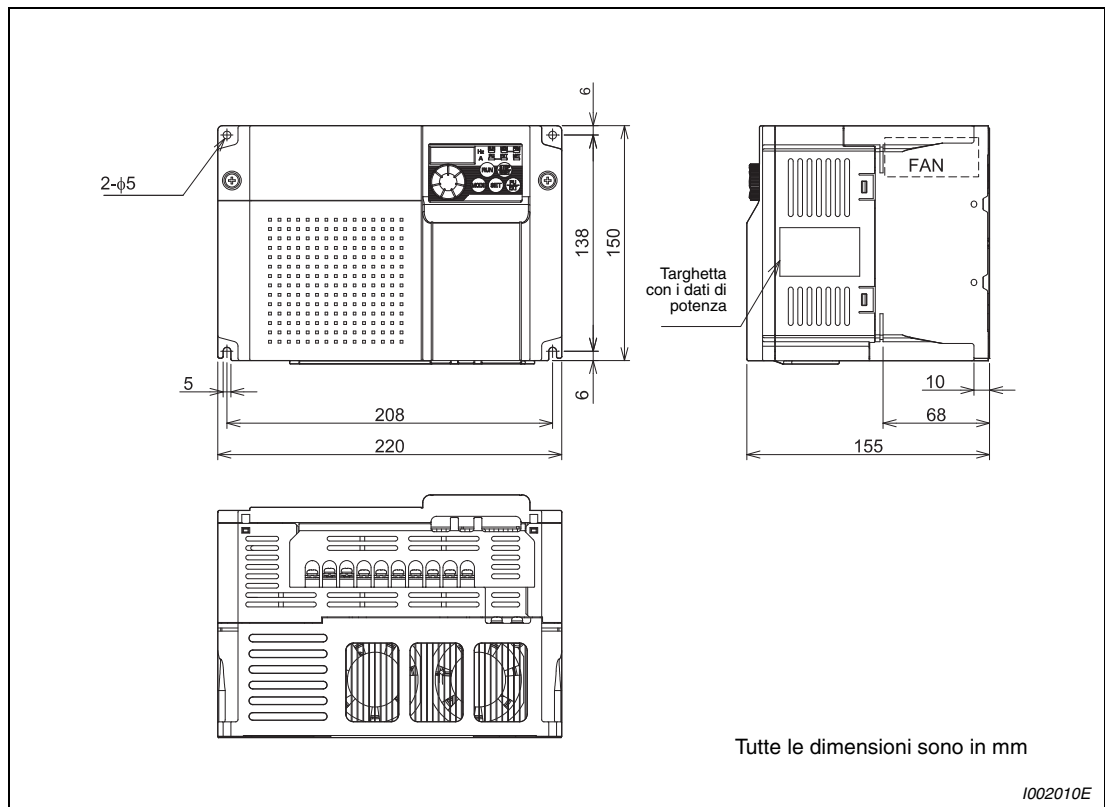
Dimensioni dell'inverter FR-D740-120SC e 160SC
